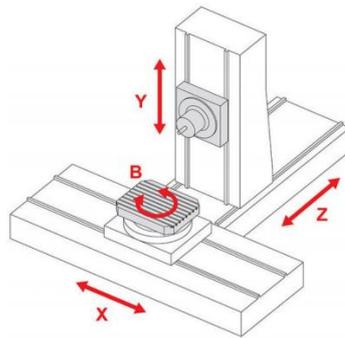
Les axes mobilisés pour une usinage à 4 axes
